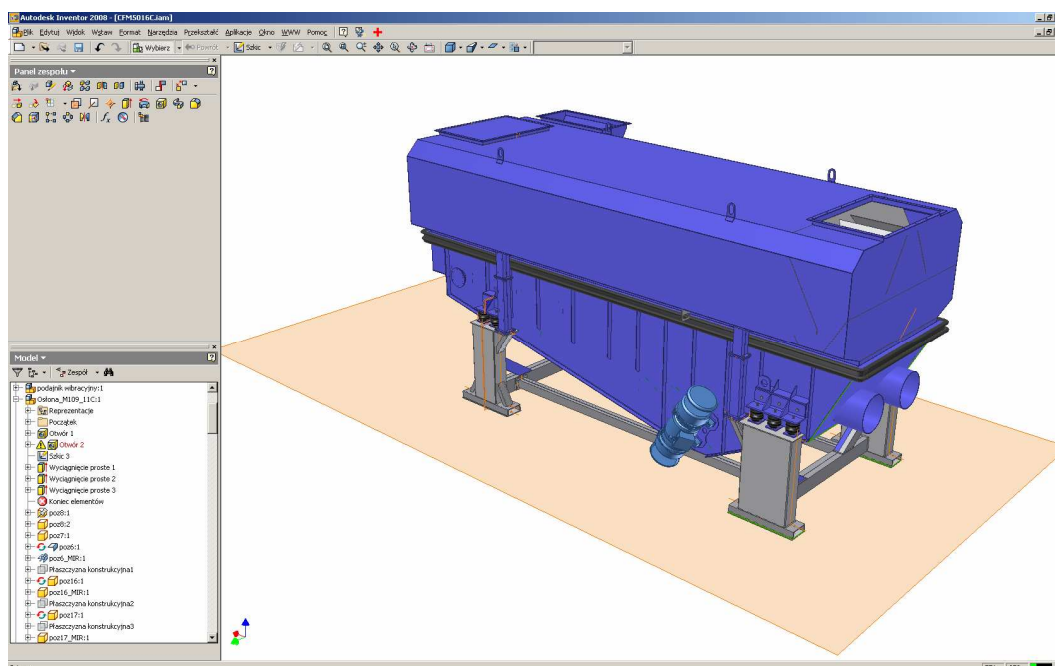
Model bryłowy przesiewacza obrotowego POS-80
